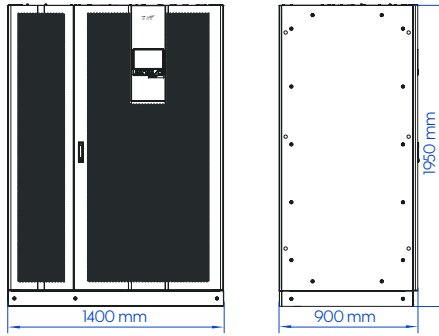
Dimensiones del UPS-IND HF 13500 y 13600 (500 y 600 kVA)
